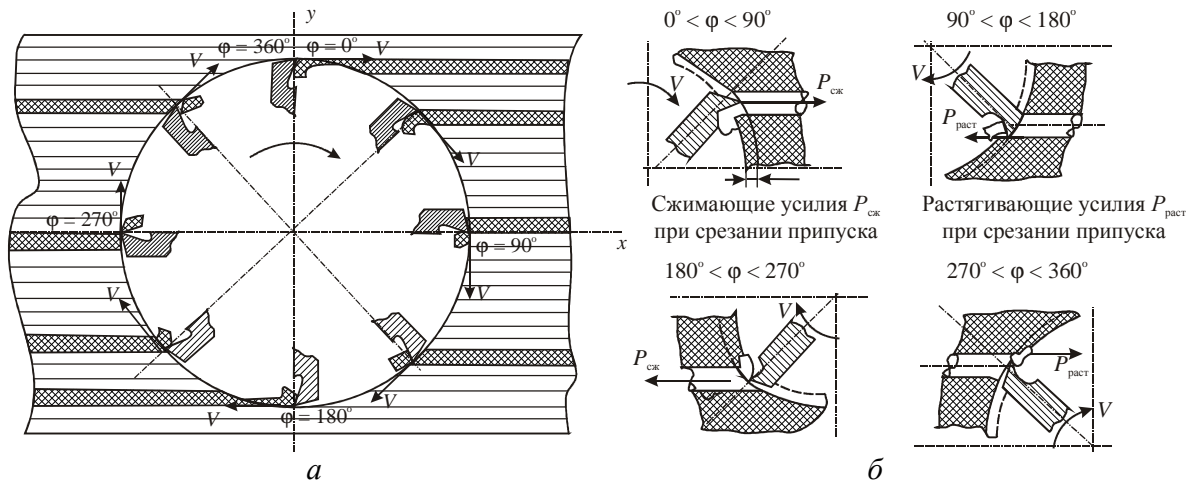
Схема срезания припуска режущим клином сверла волокон наполнителя:
